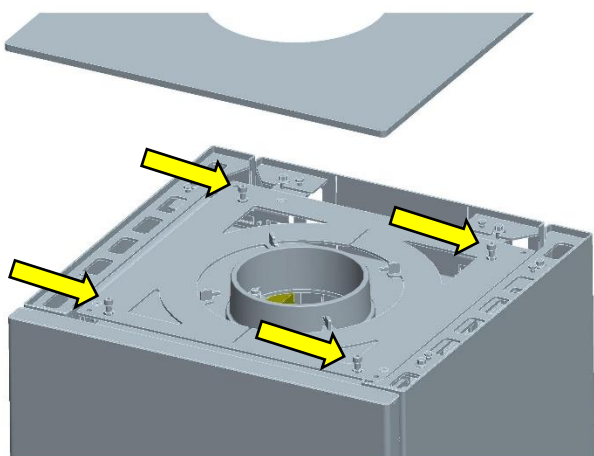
Retirer le couvercle en acier, retirer les vis de support
